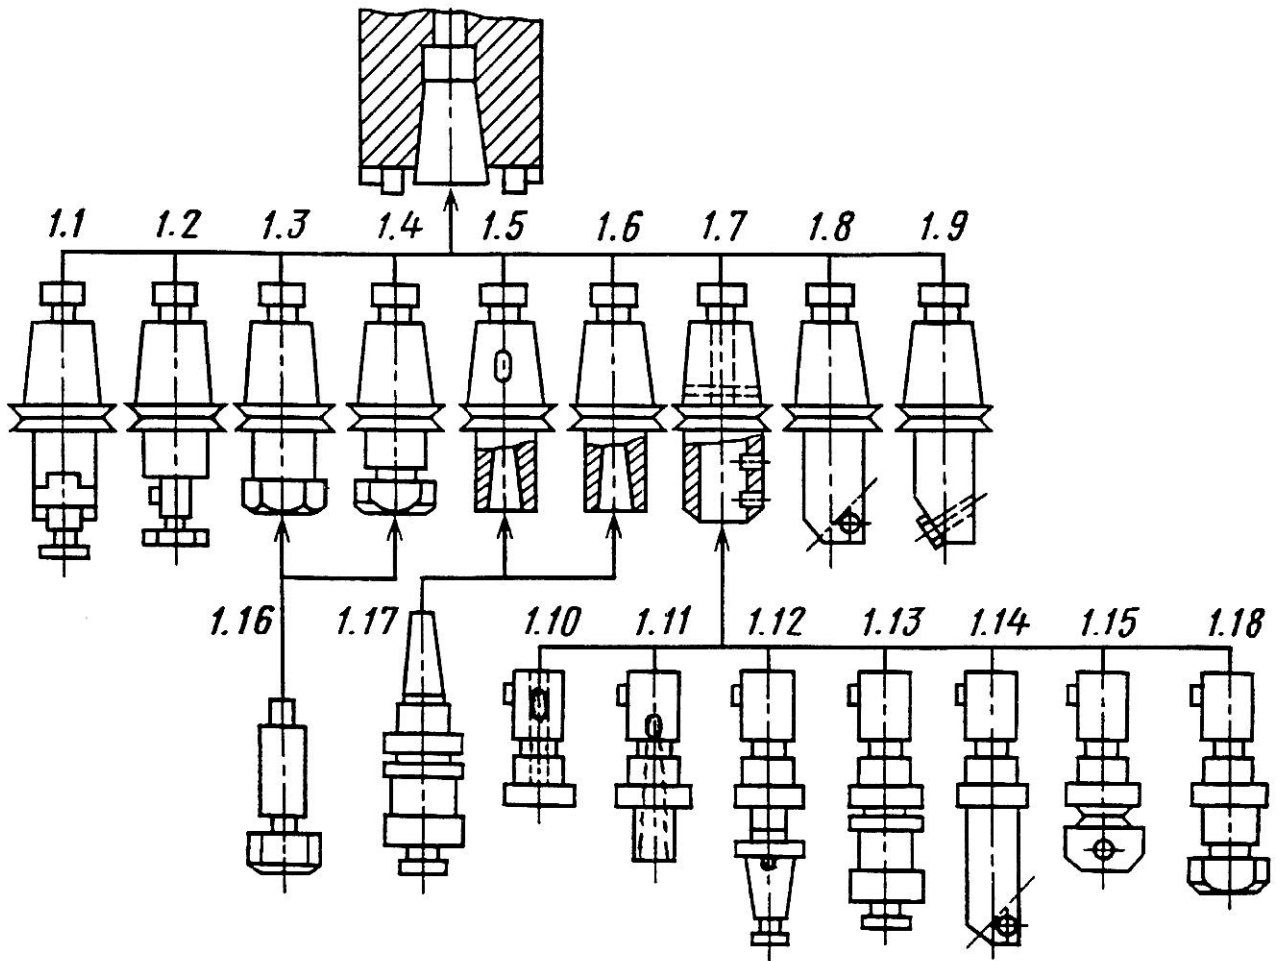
Система стандартного вспомогательного инструмента для станков сверльно-расточной и фрезерной групп: 1.1. Оправка с конусом 7:24 для насадных фрез с поперечной шпонкой. 1.2. Оправка с конусом 7:24 для насадных фрез с продольной шпонкой. 1.3. Патрон с конусом 7:24 цанговый с диапазоном зажима 20...40мм. 1.4. Патрон с конусом 7:24 цанговый с диапазоном зажима 5..20мм. 1.5. Втулка с конусом 7:24 переходная для инструмента с конусом Морзе с лапкой. 1.6. Втулка с конусом 7:24 переходная для инструмента с конусом Морзе с резьбовым отверстием. 1.7. Базовый агрегат с конусом 7:24 для сменных агрегатов. 1.8. Оправка с конусом 7:24 расточная для лучистового растачивания. 1.9. Оправка с конусом 7:24 расточная для чистового растачивания. 1.10. Сменный агрегат с внутренним конусом Морзе. 1.11. Сменный агрегат с внутренним конусом Морзе удлиненный. 1.12. Сменный агрегат для насадных разверток. 1.13. Сменный агрегат для нарезания резьбы метчиками. 1.14. Сменный агрегат для растачивания. 1.15. Сменный агрегат с поперечным суппортом для растачивания. 1.16. Сменный агрегат с цанговым зажимом 3-12мм. 1.17. Сменный агрегат с конусом Морзе для нарезания резьбы метчиками. 1.18. Сменный агрегат с цанговым зажимом 5 - 20мм.
